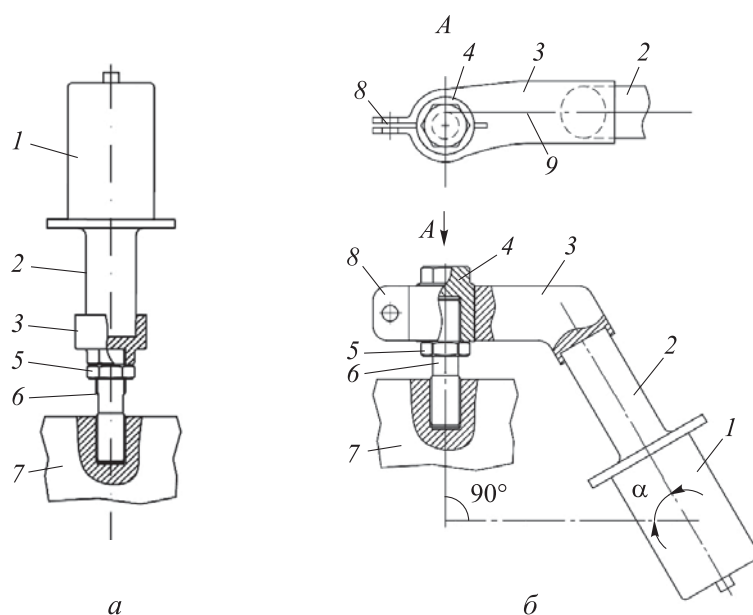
Конструкция экспериментальных приспособлений, реализующих ввод низкочастотных ультразвуковых колебаний с торцевой (а) и боковой (под углом α) поверхности (б) шпильки:
